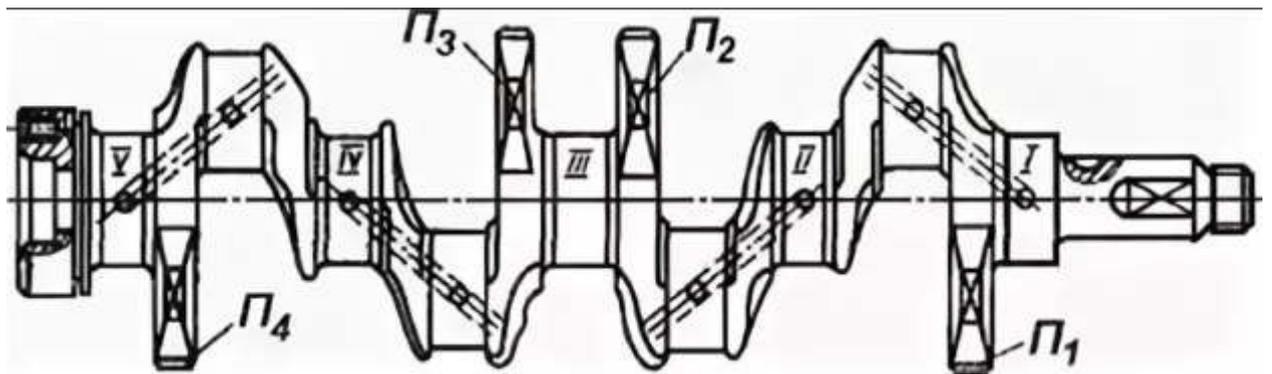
Коленчатый вал в КамАЗ – 740.
